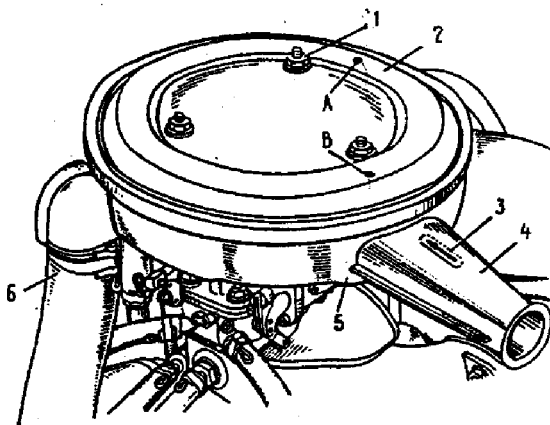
Conjunto do filtro de ar: 1 - porca de fixação; 2 - tampa do filtro; 3 - seta reguladora; 4 - tomada de ar para temperaturas altas; 5 - carcaça do filtro; 6 - mangueira de tomada de ar para baixas temperaturas; A - marca azul - quente; B - marca vermelha - frio.
